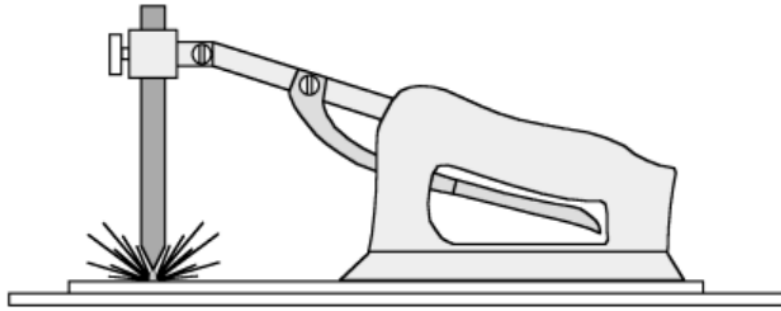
Primeiro sistema de soldadura por arco com eletrodo de carvão patenteado, de acordo com a patente de Bernardos [52]
